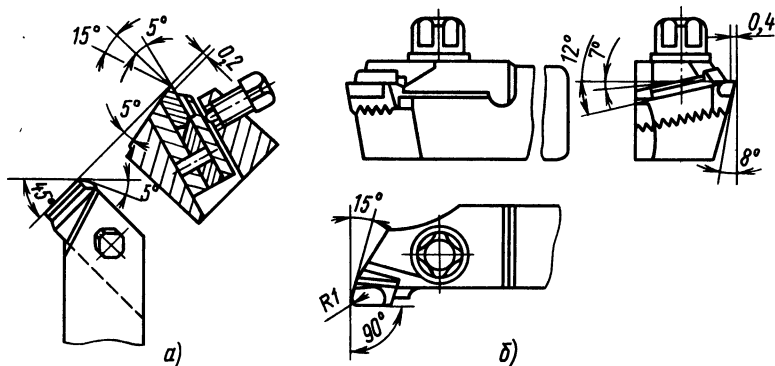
Расточные резцы с механическим креплением твердосплавных пластин:
